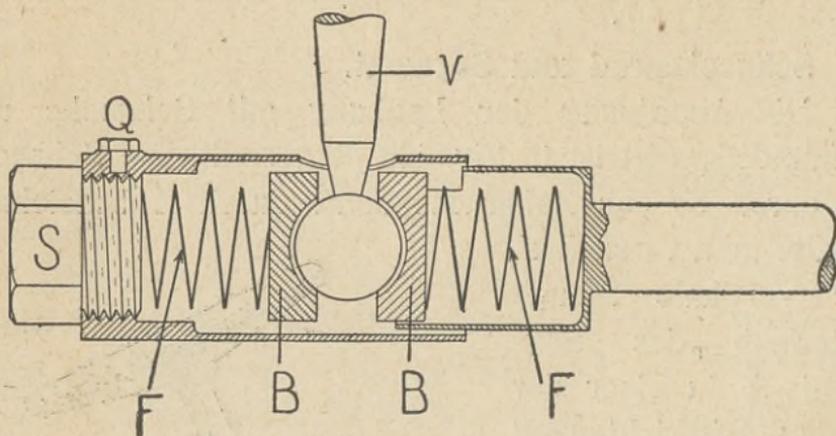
Die Stoßfederung der unverrückbaren Lenkung.
